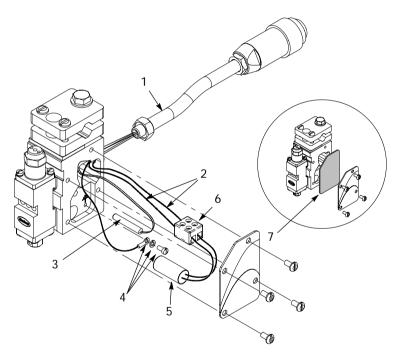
Remplacement d'une résistance chauffante (la figure représente un pistolet ClassicBlue)
